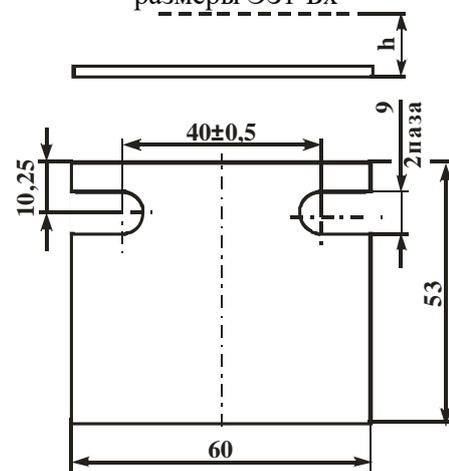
Габаритные и присоединительные размеры ЭЗ2
